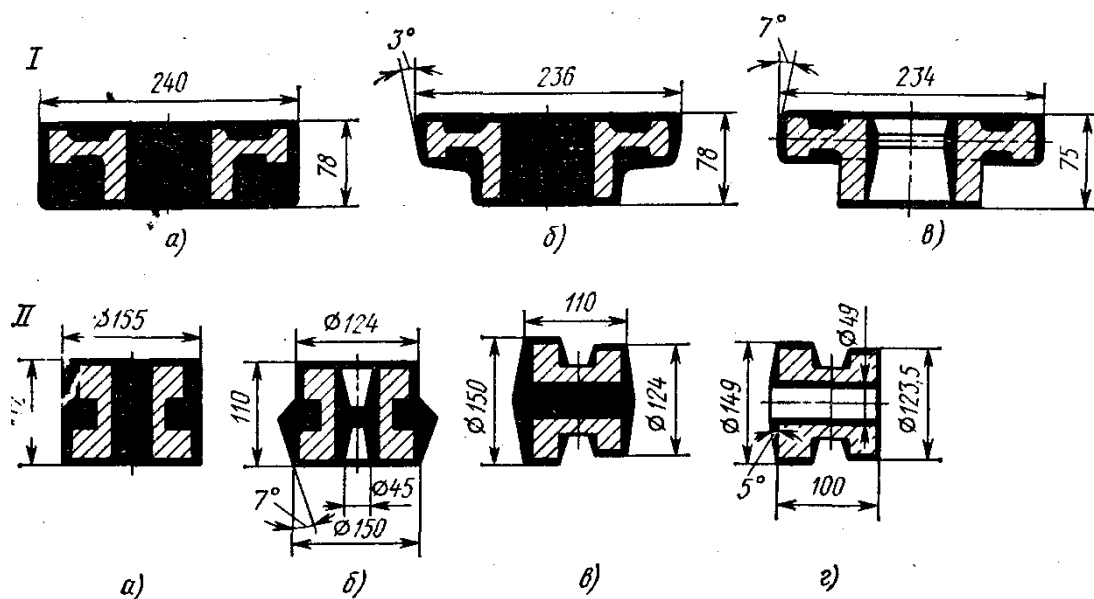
Схемы изготовления заготовок для зубчатых колес
